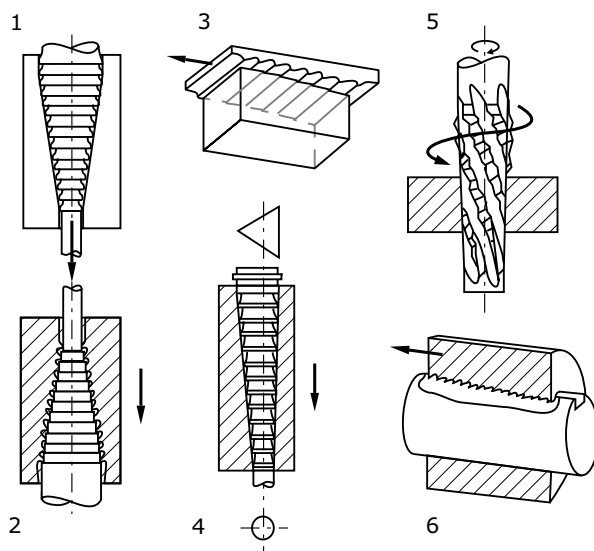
reZ) 1: Innenrundräumen; 2: Aussenrundräumen; 3: Aussenplanräumen; 4: Innen-Profilräumen; 5: Innen-Schraubräumen; 6: Aussen-Nuten-Räumen; A: Werkstück; B: Werkzeug; C: Ausgangsquerschnitt; D: Endquerschnitt
